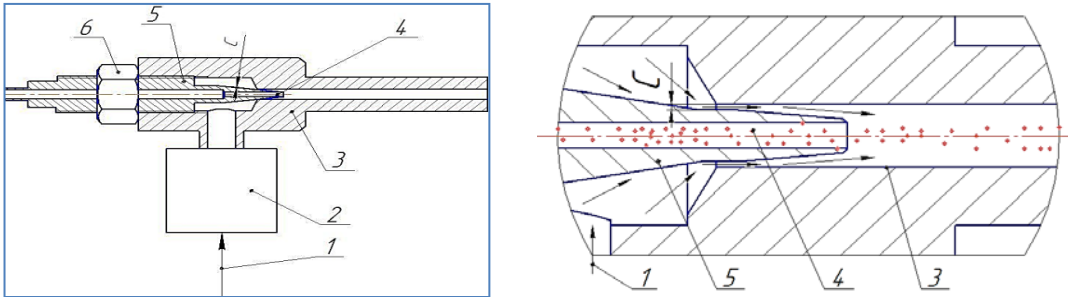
Принципова схема головки для напилювання порошку газодинамічного пристрою нанесення функціональних покриттів: 1 — лінія подачі стиснутого газу; 2 — нагрівач газу; 3 — сопло; 4 — канал подачі матеріалу для напилювання; 5 — форсунка; 6 — гайка-фіксатор
